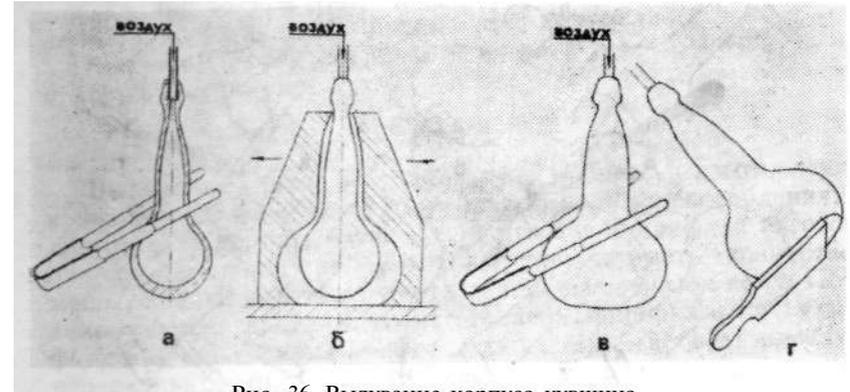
Выдувание корпуса кувшина (а, б — в форму; в, г — свободное).
